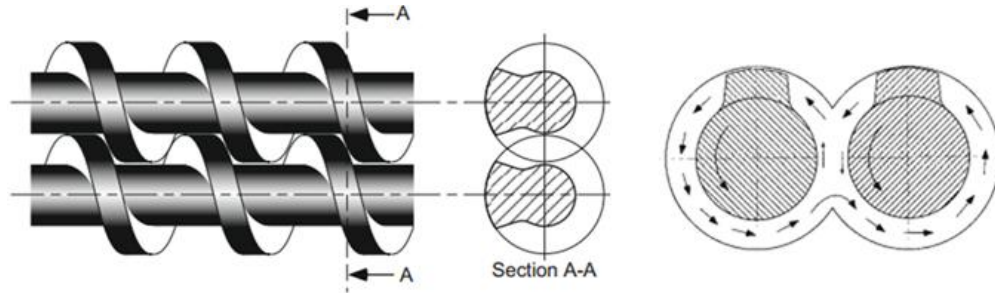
Doble tornillo corrotante de alto grado de engrane. [15]
